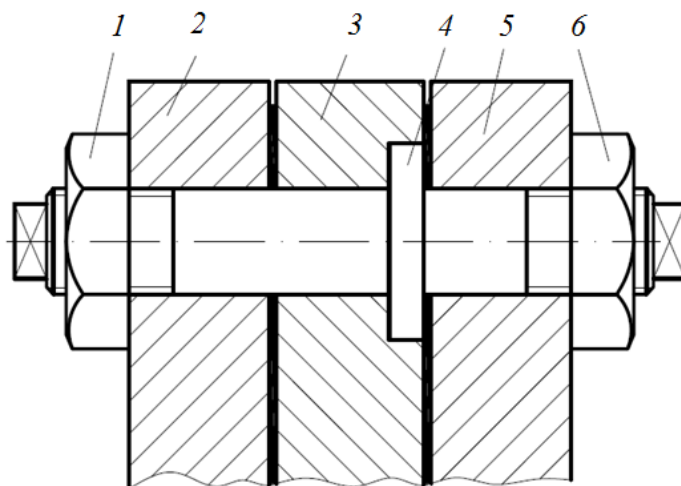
Кріплення трубної дошки шпильками з упорним буртиком
